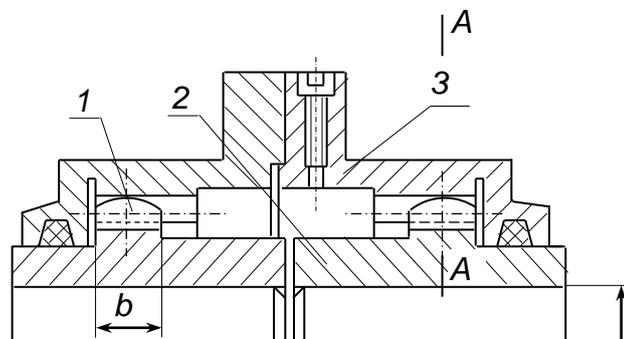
Конструкция зубчатой муфты: 1, 2 – втулки с внешними зубьями; 3 – составная обойма с внутренними зубьями
